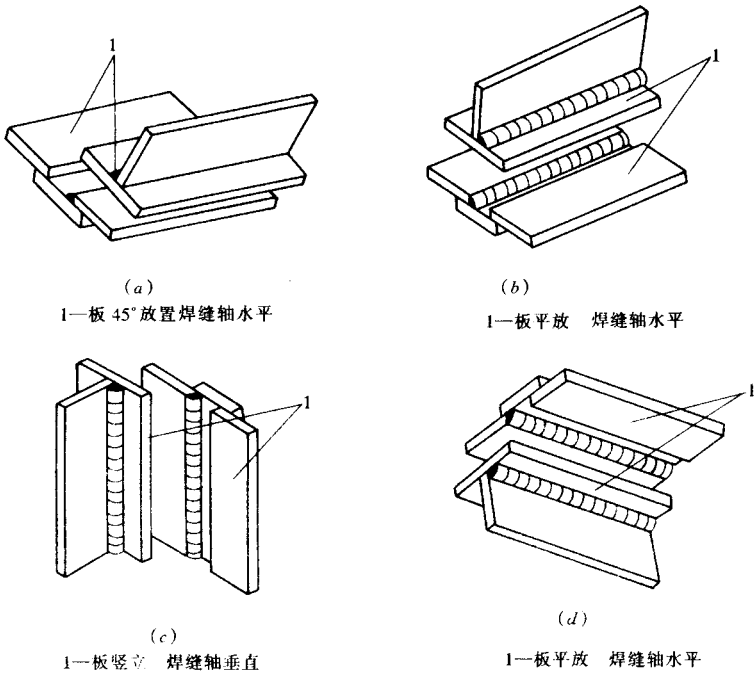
板材角接接头焊接位置示意
